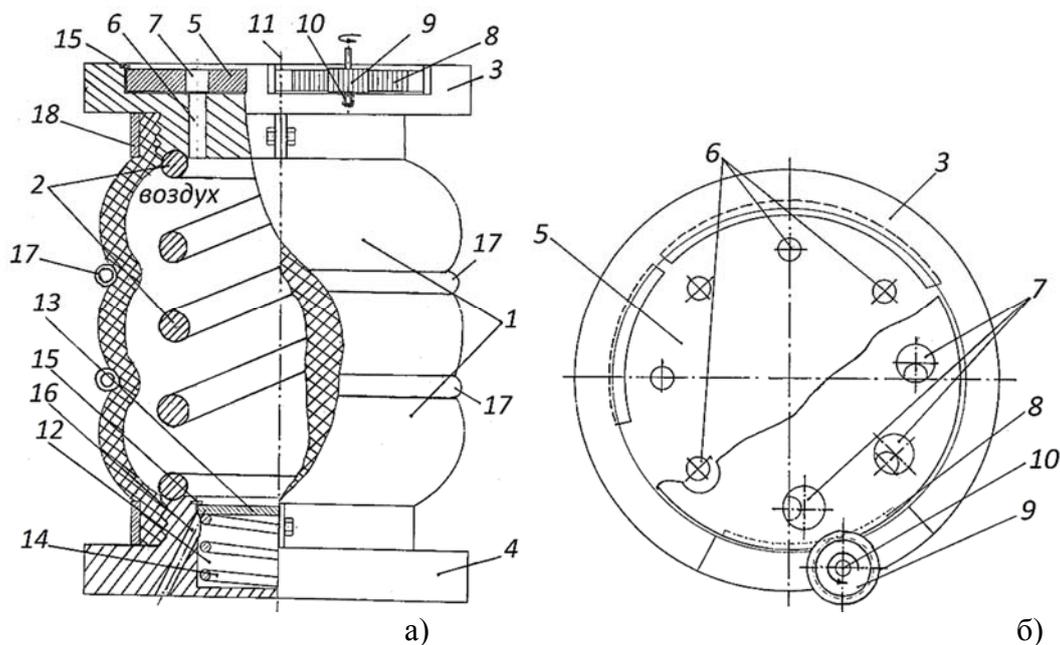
Подвеска транспортного средства: а) - вид сбоку; б) - вид сверху
